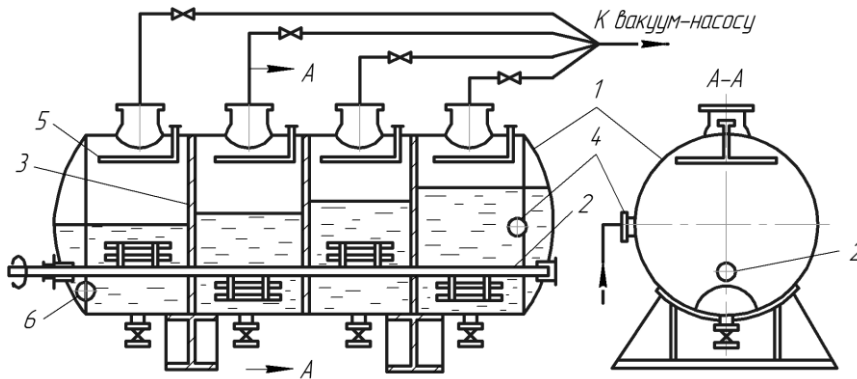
Горизонтальный многоступенчатый вакуум-кристаллизатор: 1 – цилиндрический корпус; 2 – лопастная мешалка; 3 – перегородка; 4 – штуцер для подачи раствора; 5 – оросительное устройство; 6 – штуцер для вывода суспензии [8]
